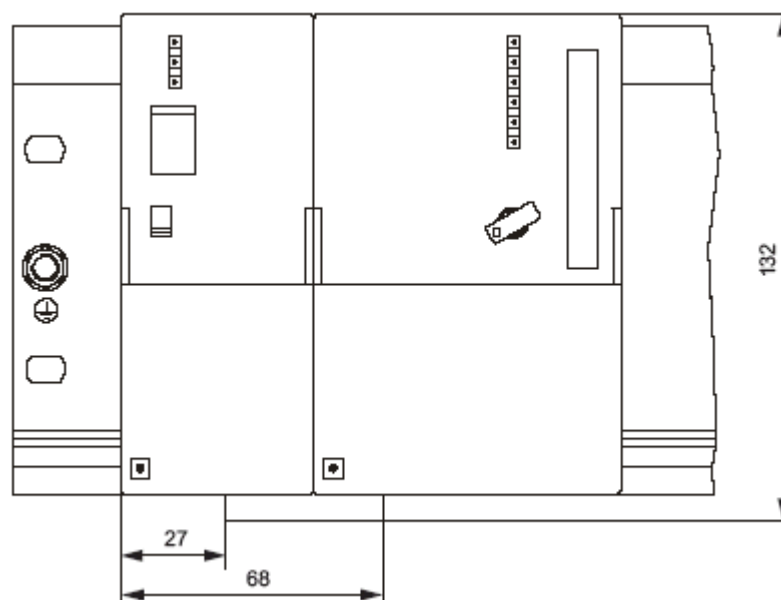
Габаритный чертеж блока питания PS 307; 5 A с CPU 313/314/315/315-2 DP, вид спереди
